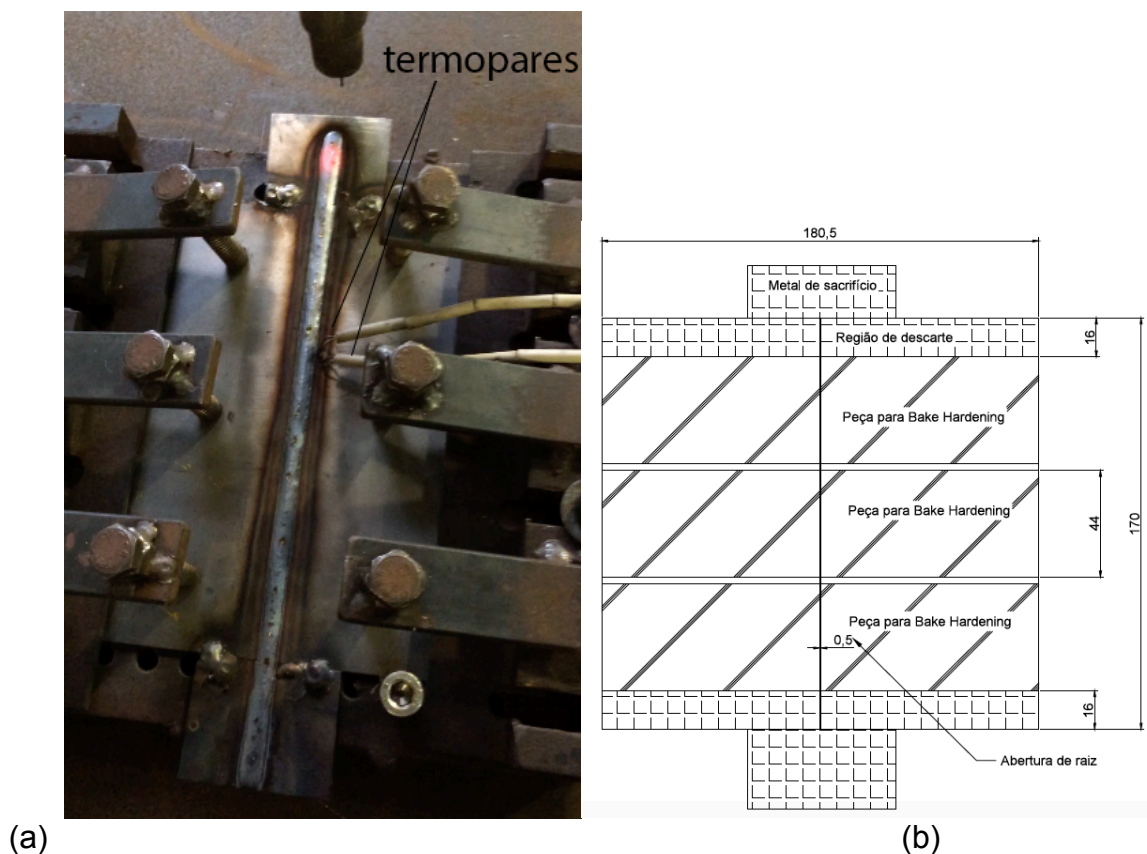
(a) Sistema para soldagem dos espécimes. (b) Croqui dos espécimes soldados.
